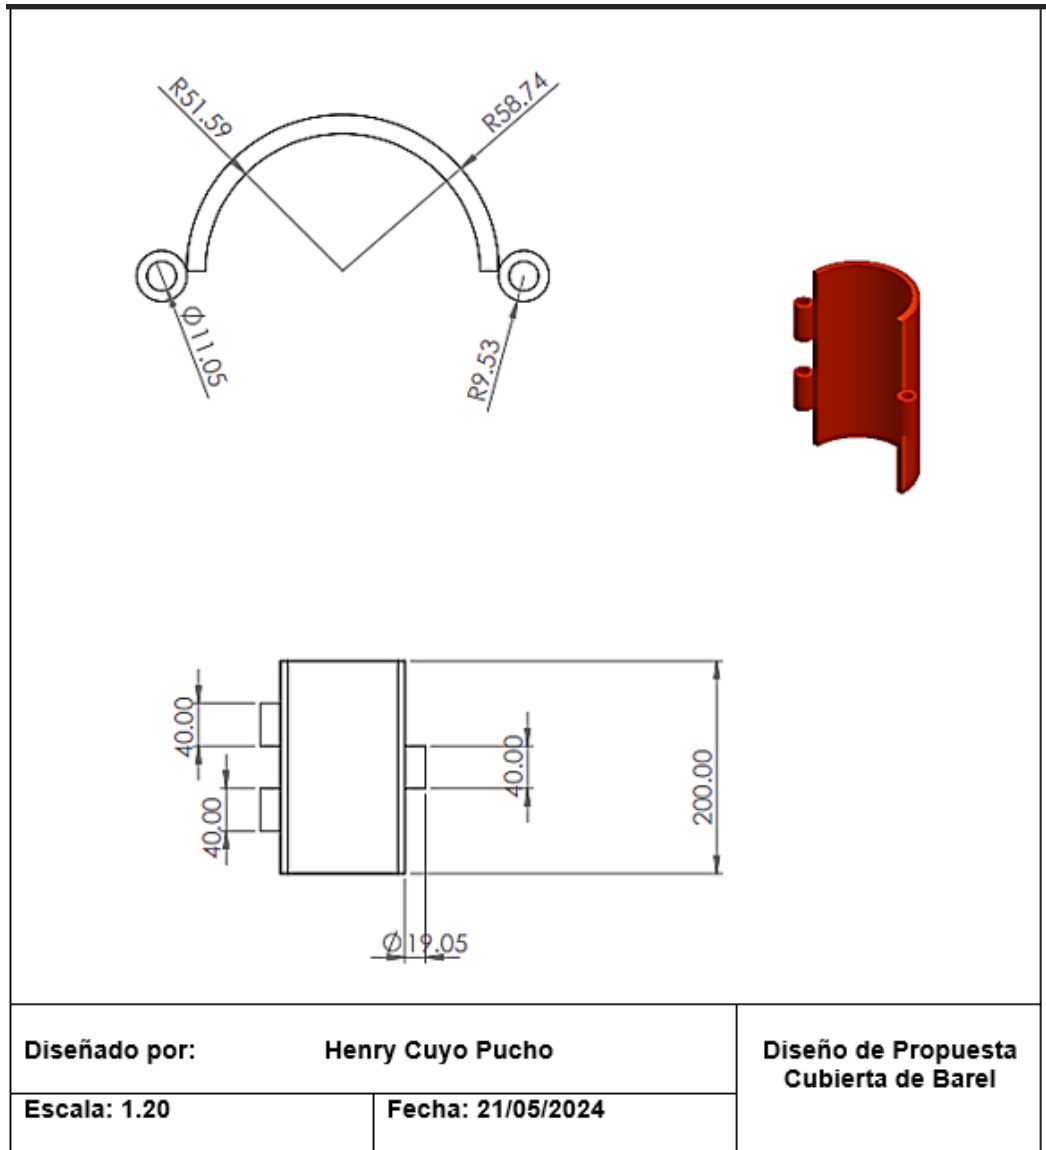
Plano de cubierta de Barel para armado de Covered Base for Barel – CBB.
